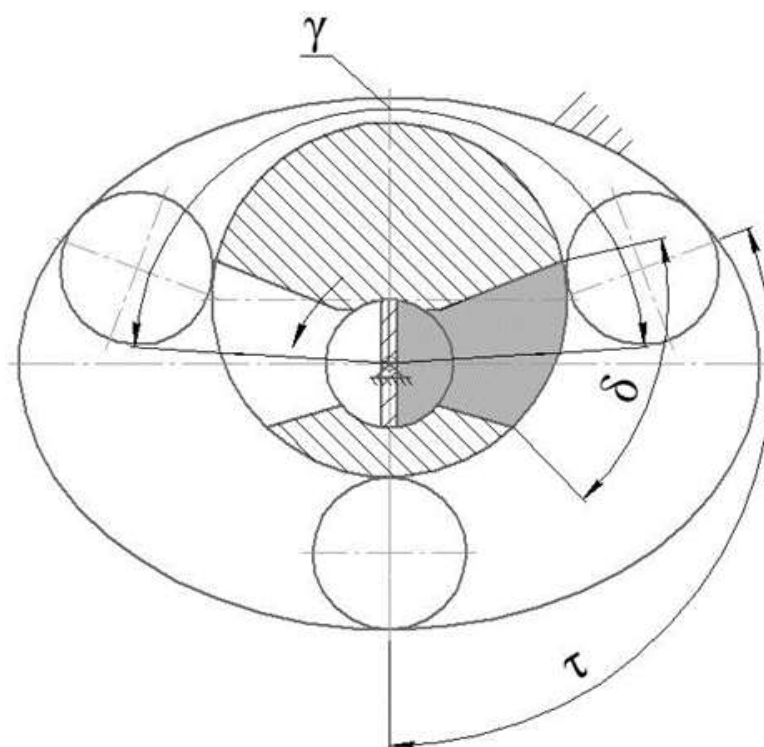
ПРМ 2-1 с каналами в цилиндрической части солнечной шестерни [95]
